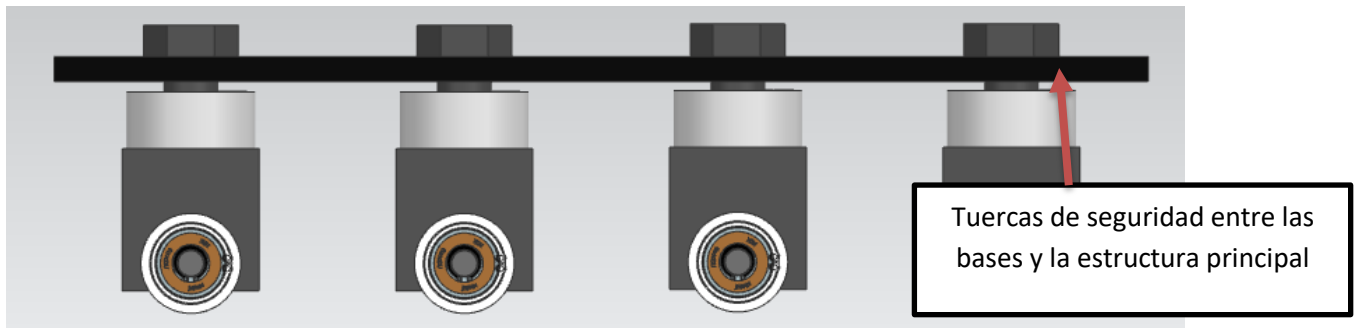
Detalle aseguramiento Trolley y estructura principal. Fuente propia.
